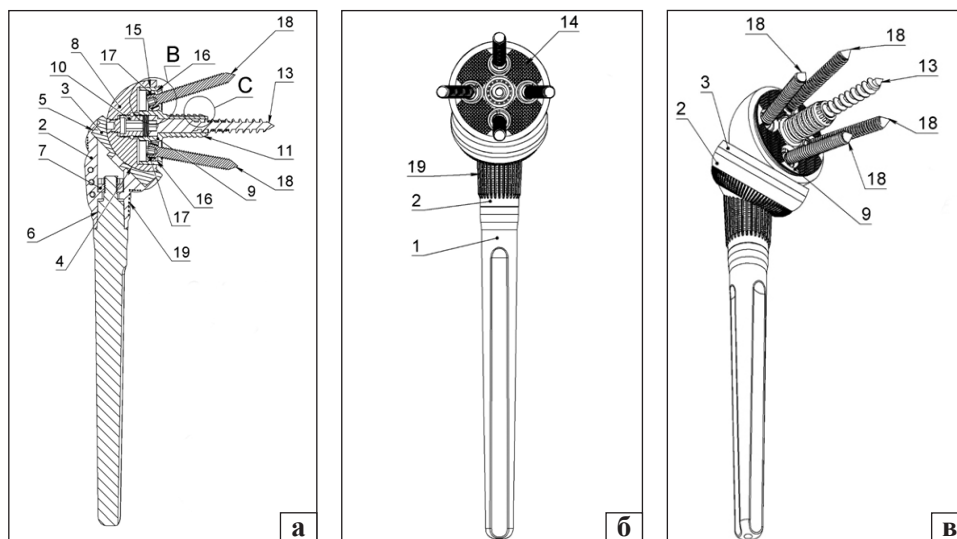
Реверсивний модульний ендопротез плечового суглоба: 1 — ніжка, виготовлена у вигляді конусного трилопаткового стрижня; 2 — пориста проксимальна частина, надрукована на 3D-принтері з титанового порошку (аналог BT-5); 3 — вкладиш, виготовлений із ПEEK у вигляді конічного циліндра; 4 — увігнута сферична поверхня вкладиша; 5 — конус Морзе; 6 — проксимальна частина ендопротеза фіксується за допомогою конуса Морзе до проксимальної частини ніжки; 7 — фіксуюча гайка; 8 — гленоїдальна головка; 9 — гленоїдальна опорна пластина; 9 — зовнішній край опорної пластини, виконаний у вигляді конуса Морзе; 10 — фіксуючий гвинт; 11 — центральний стрижень; 12 — конусоподібні ребра з довжиною ребра пори 350–500 мкм; 13 — центральний гвинт; 14 — пориста поверхня гленоїдальної опорної пластини з довжиною ребра пори 350–500 мкм на глибину 2 мм; 15 — зовнішня поверхня гленоїдальної опорної пластини у вигляді конуса Морзе; 16 — сферичні отвори гленоїдальної опори; 17 — сферичні шайби; 18 — гвинти; 19 — проксимальна частина з ребристою пористою зовнішньою поверхнею [30]; а) зовнішній вигляд; б) фронтальна проекція; в) вигляд збоку
